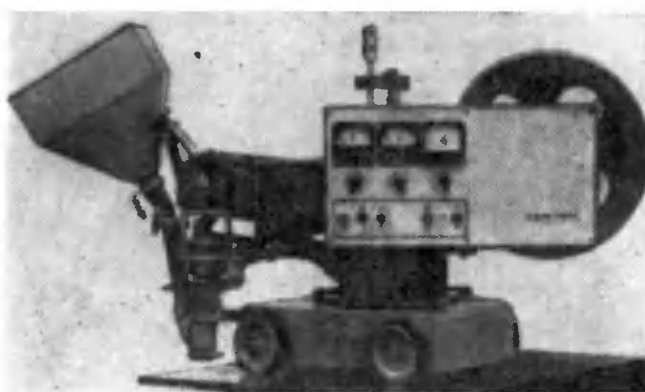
Сварочный автомат АДФ-1001.
